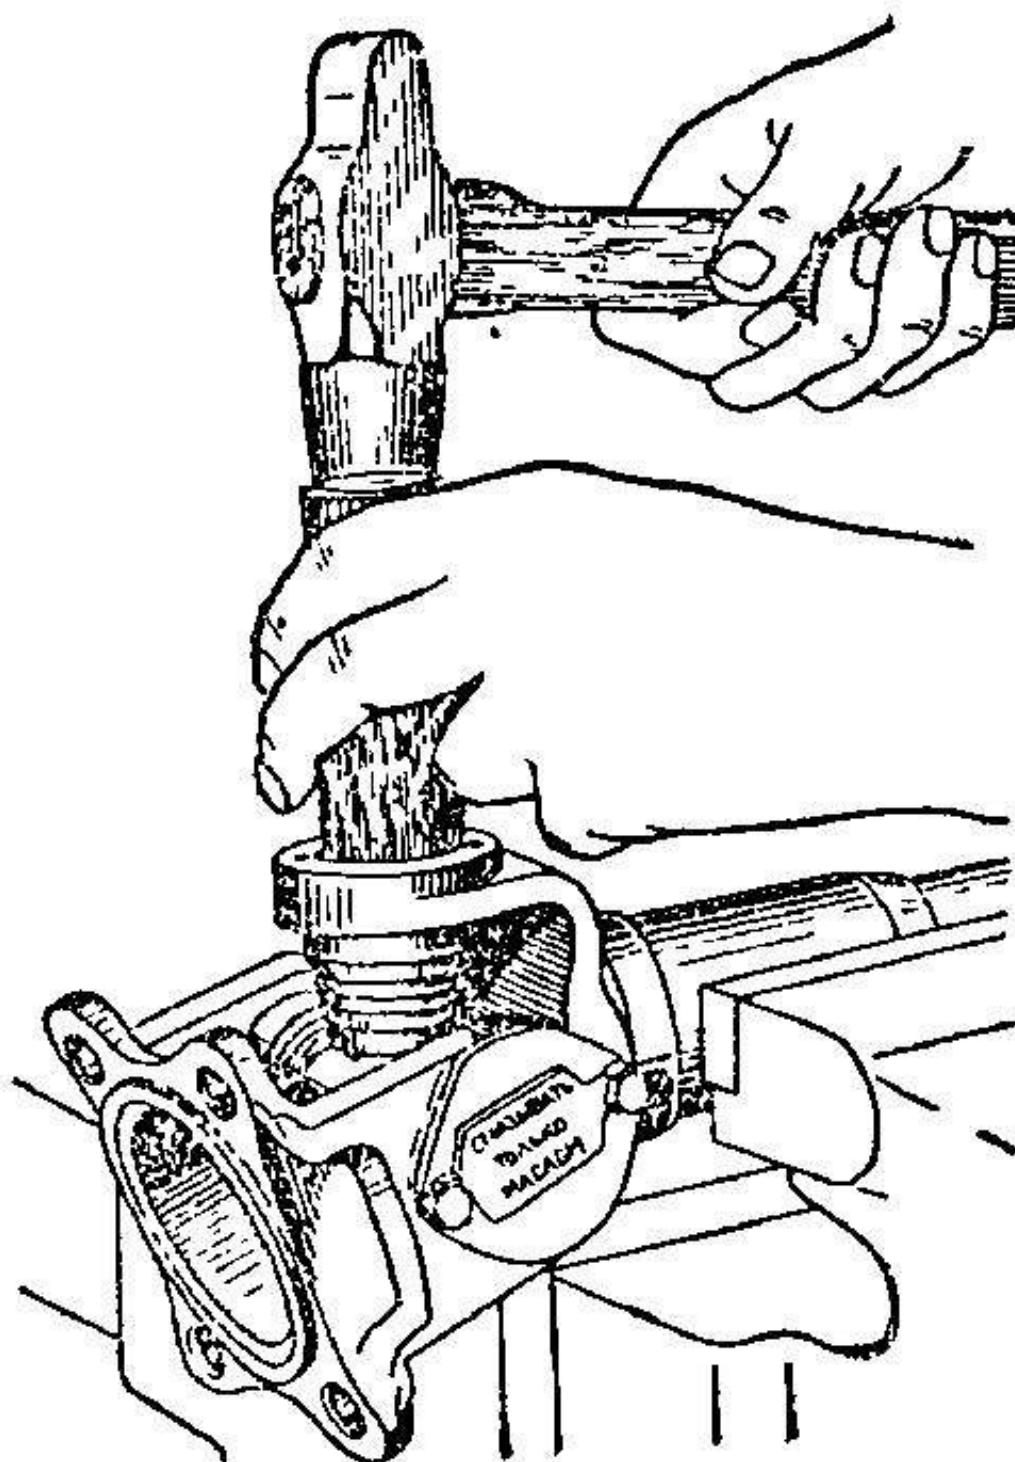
Выпрессовка подшипников карданного шарнира.
